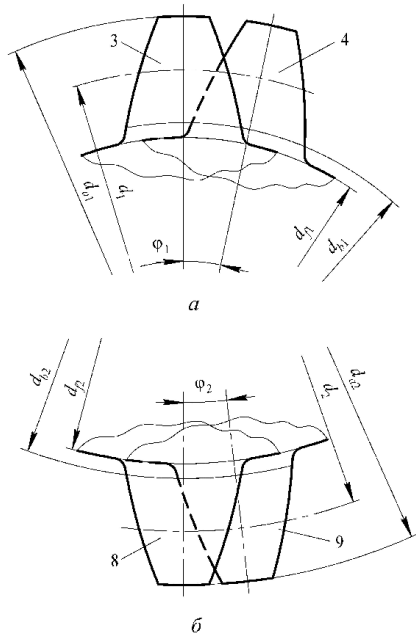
Поворот зубьев 1 шестерни (а) и зуба 2 колеса (б) в окружном направлении венцов
